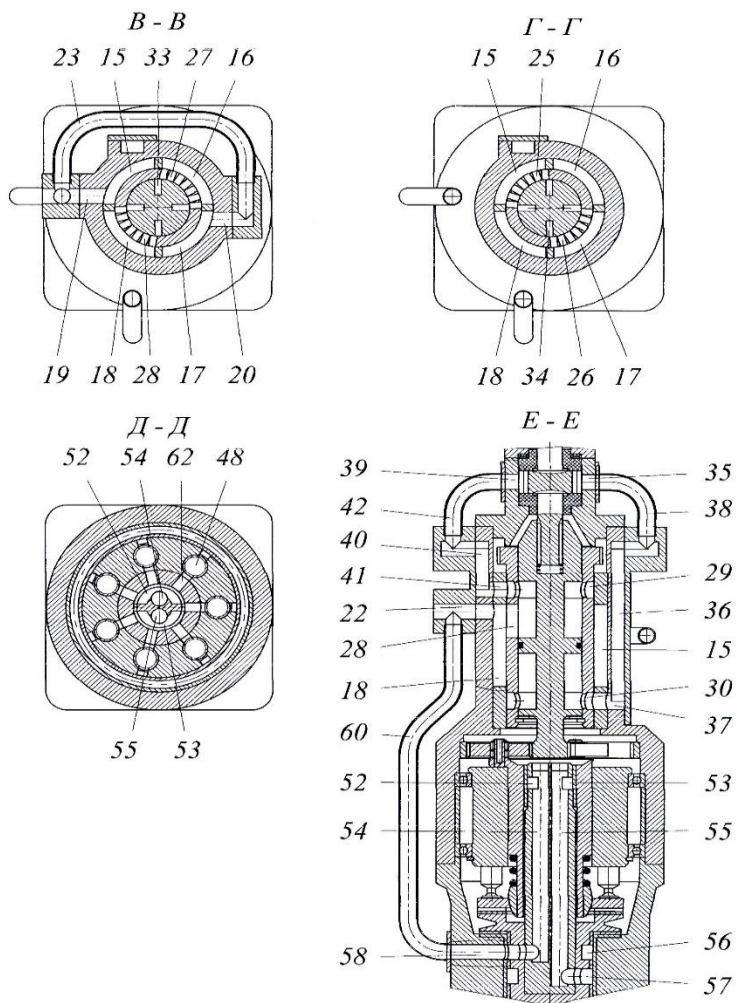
(продолжение). ОГП с планетарным редуктором в линии связи приводного вала и блока цилиндров гидромотора
